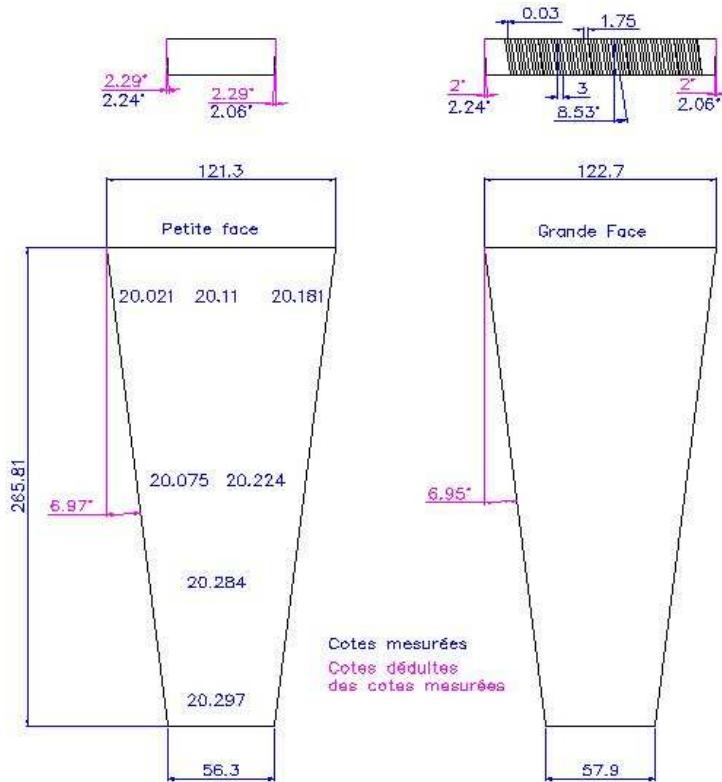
géométrie et dimensions typiques d'un scintillateur.
